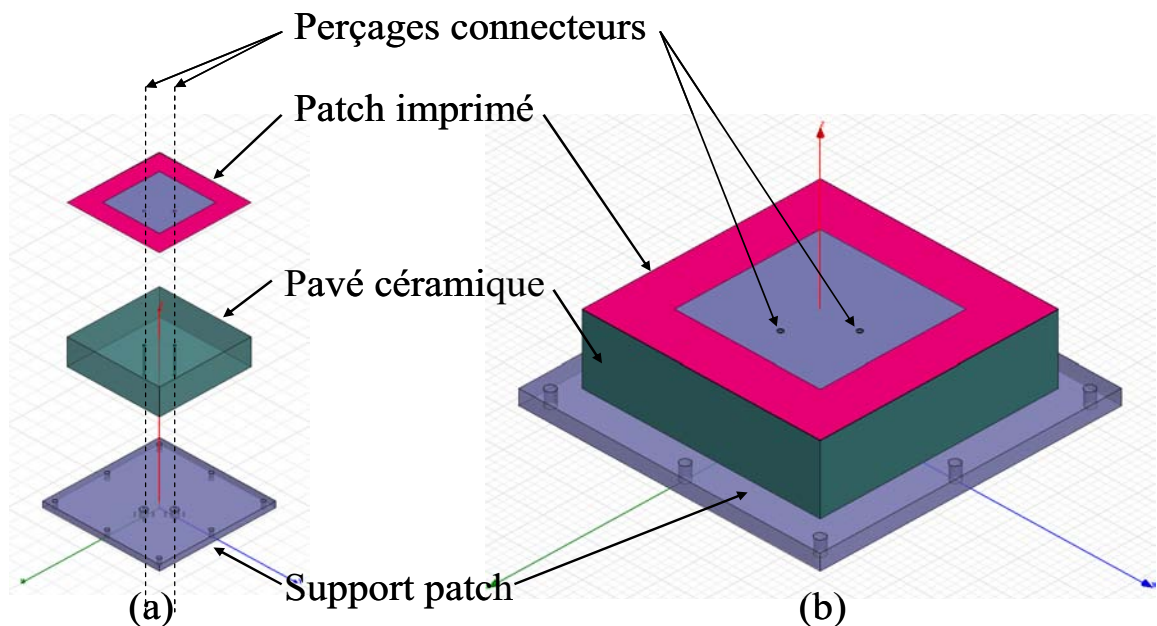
Vue 3D d'un patch sur support métallique : (a) vue éclatée, (b) vue après collage
